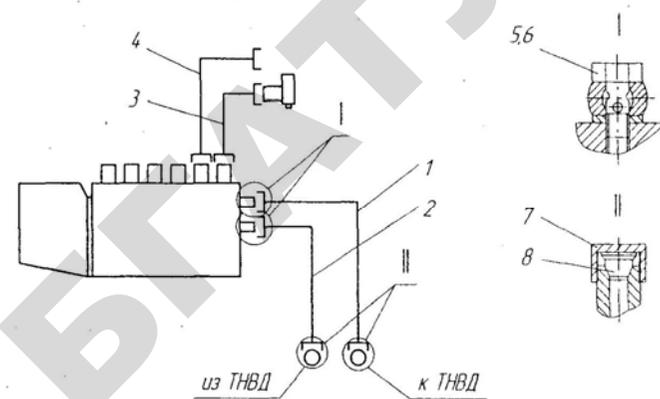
Схема соединений трубопроводов при испытании 4ТМ 8,5×10
